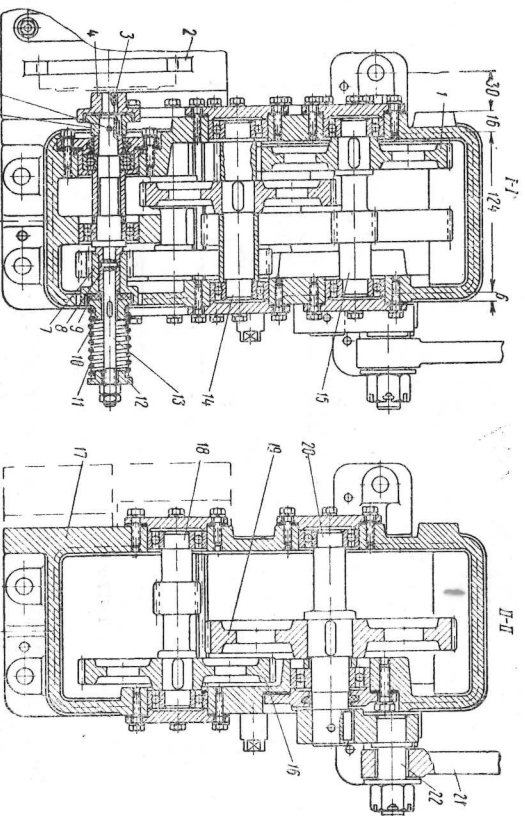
Редуктор электропривода автоматического шлагбаума (вид в разрезе)
